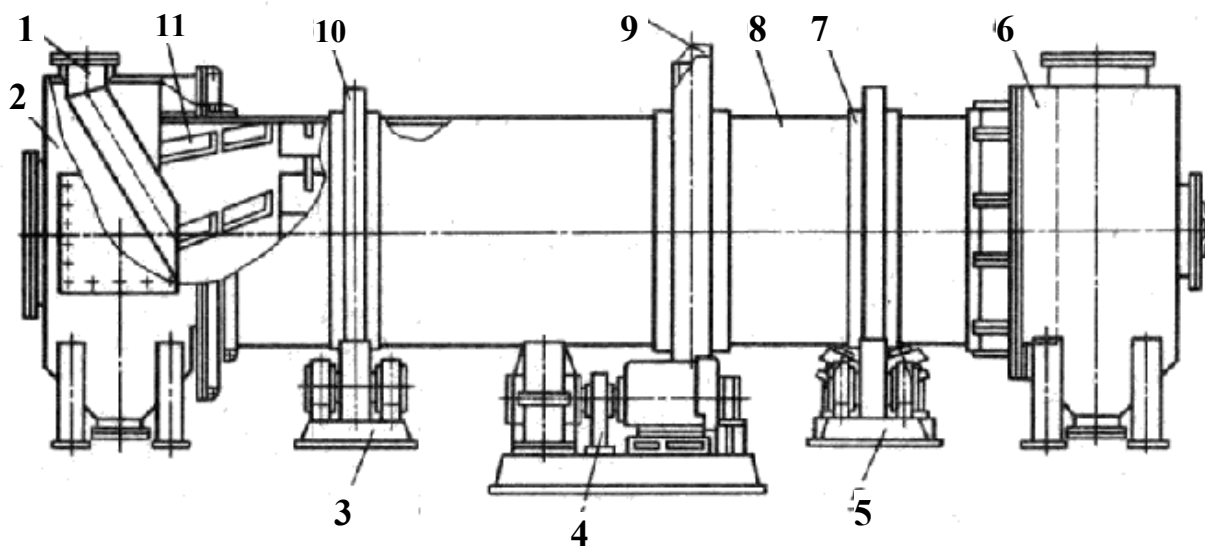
Сушильний барабан: 1 – завантажувальний лоток; 2 – завантажувальна камера; 3 – опорна рама; 4 – привід; 5 – опорно-упорна станція; 6 – розвантажувальна камера; 7 – кільцева накладка; 8 – обичайка барабана; 9 – зубчастий вінець; 10 – бандаж; 11 – приймально-гвинтова насадка
